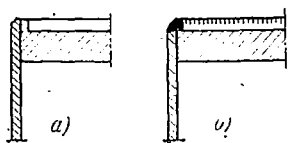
Вварка дна аргон-дуговой сваркой с отбортовкой.
